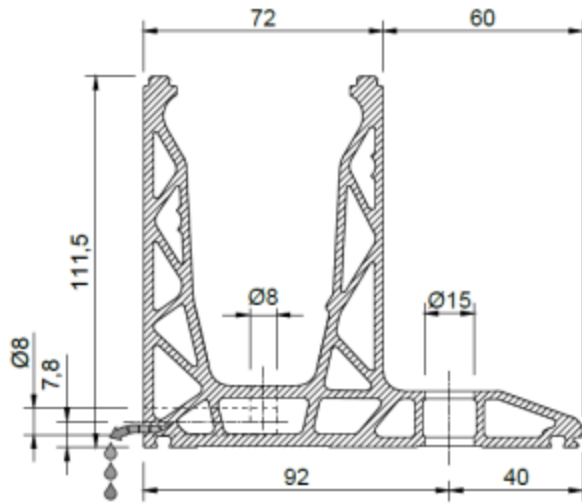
section transversale du profilé DF88DK.60 avec indication de perçage pour drainage
